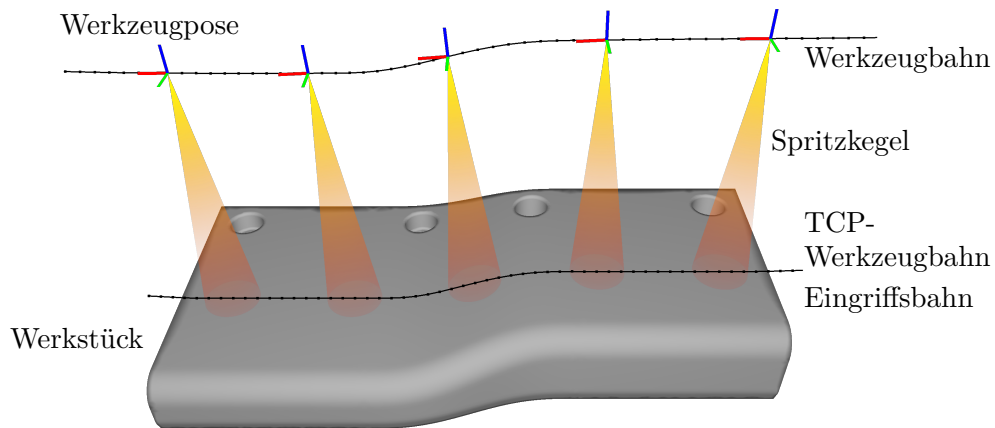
Visualisierung von verschiedenen Bahntypen. Die über einen Punkt an der Spitze der Spritzpistole definierte Werkzeughahn verläuft über dem Werkstück. Einige Werkzeugposen, die die Ausrichtung der Spritzpistole bestimmen, sowie die dort anliegenden Spritzkegel sind ebenfalls eingezeichnet. Die TCP-Werkzeughahn und die Eingriffsbahn (hier identisch) liegen idealerweise genau auf der Oberfläche des Werkstücks.
